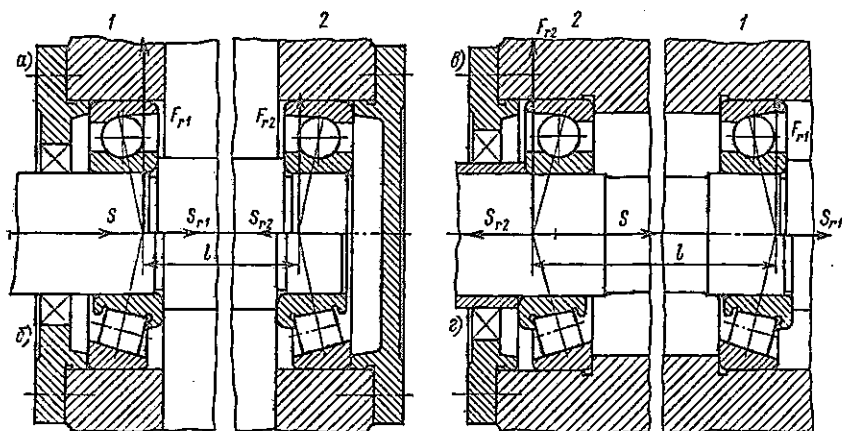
Схемы установки радиально-упорных подшипников: а, б — схемы установки «враспор»; в, г — схемы установки «вдавливаю»
